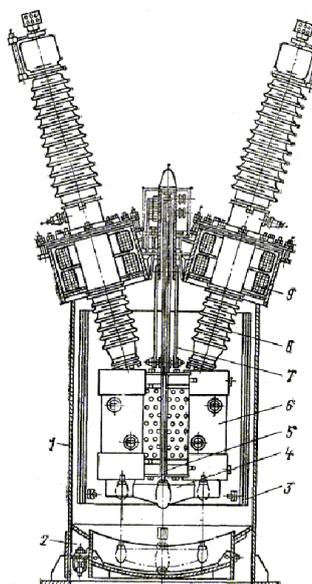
Баковый масляный выключатель на напряжение 110 кВ:
